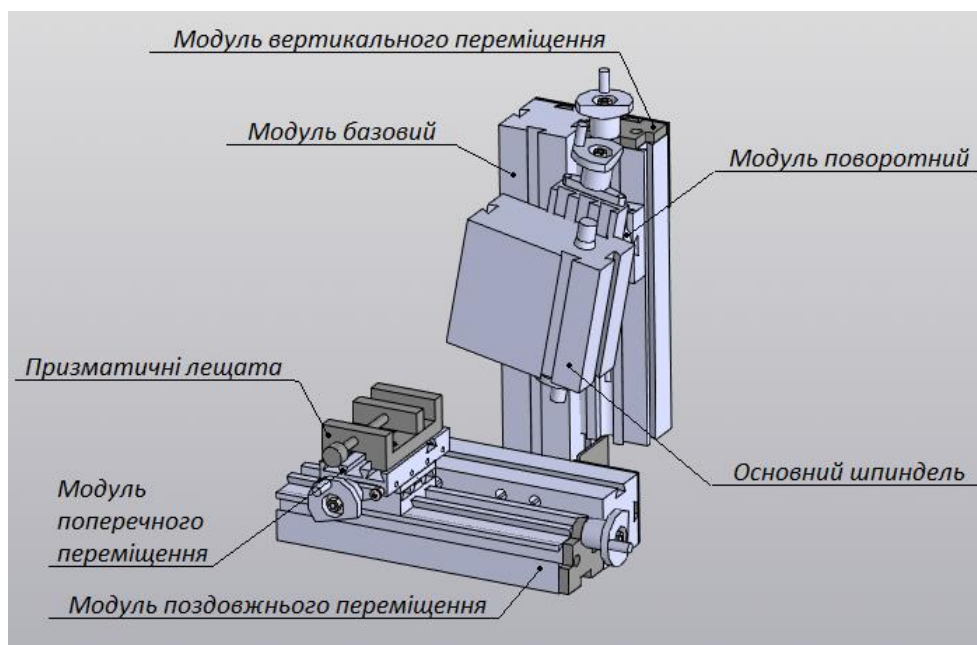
Багатокординатний фрезерний верстат у зборі
